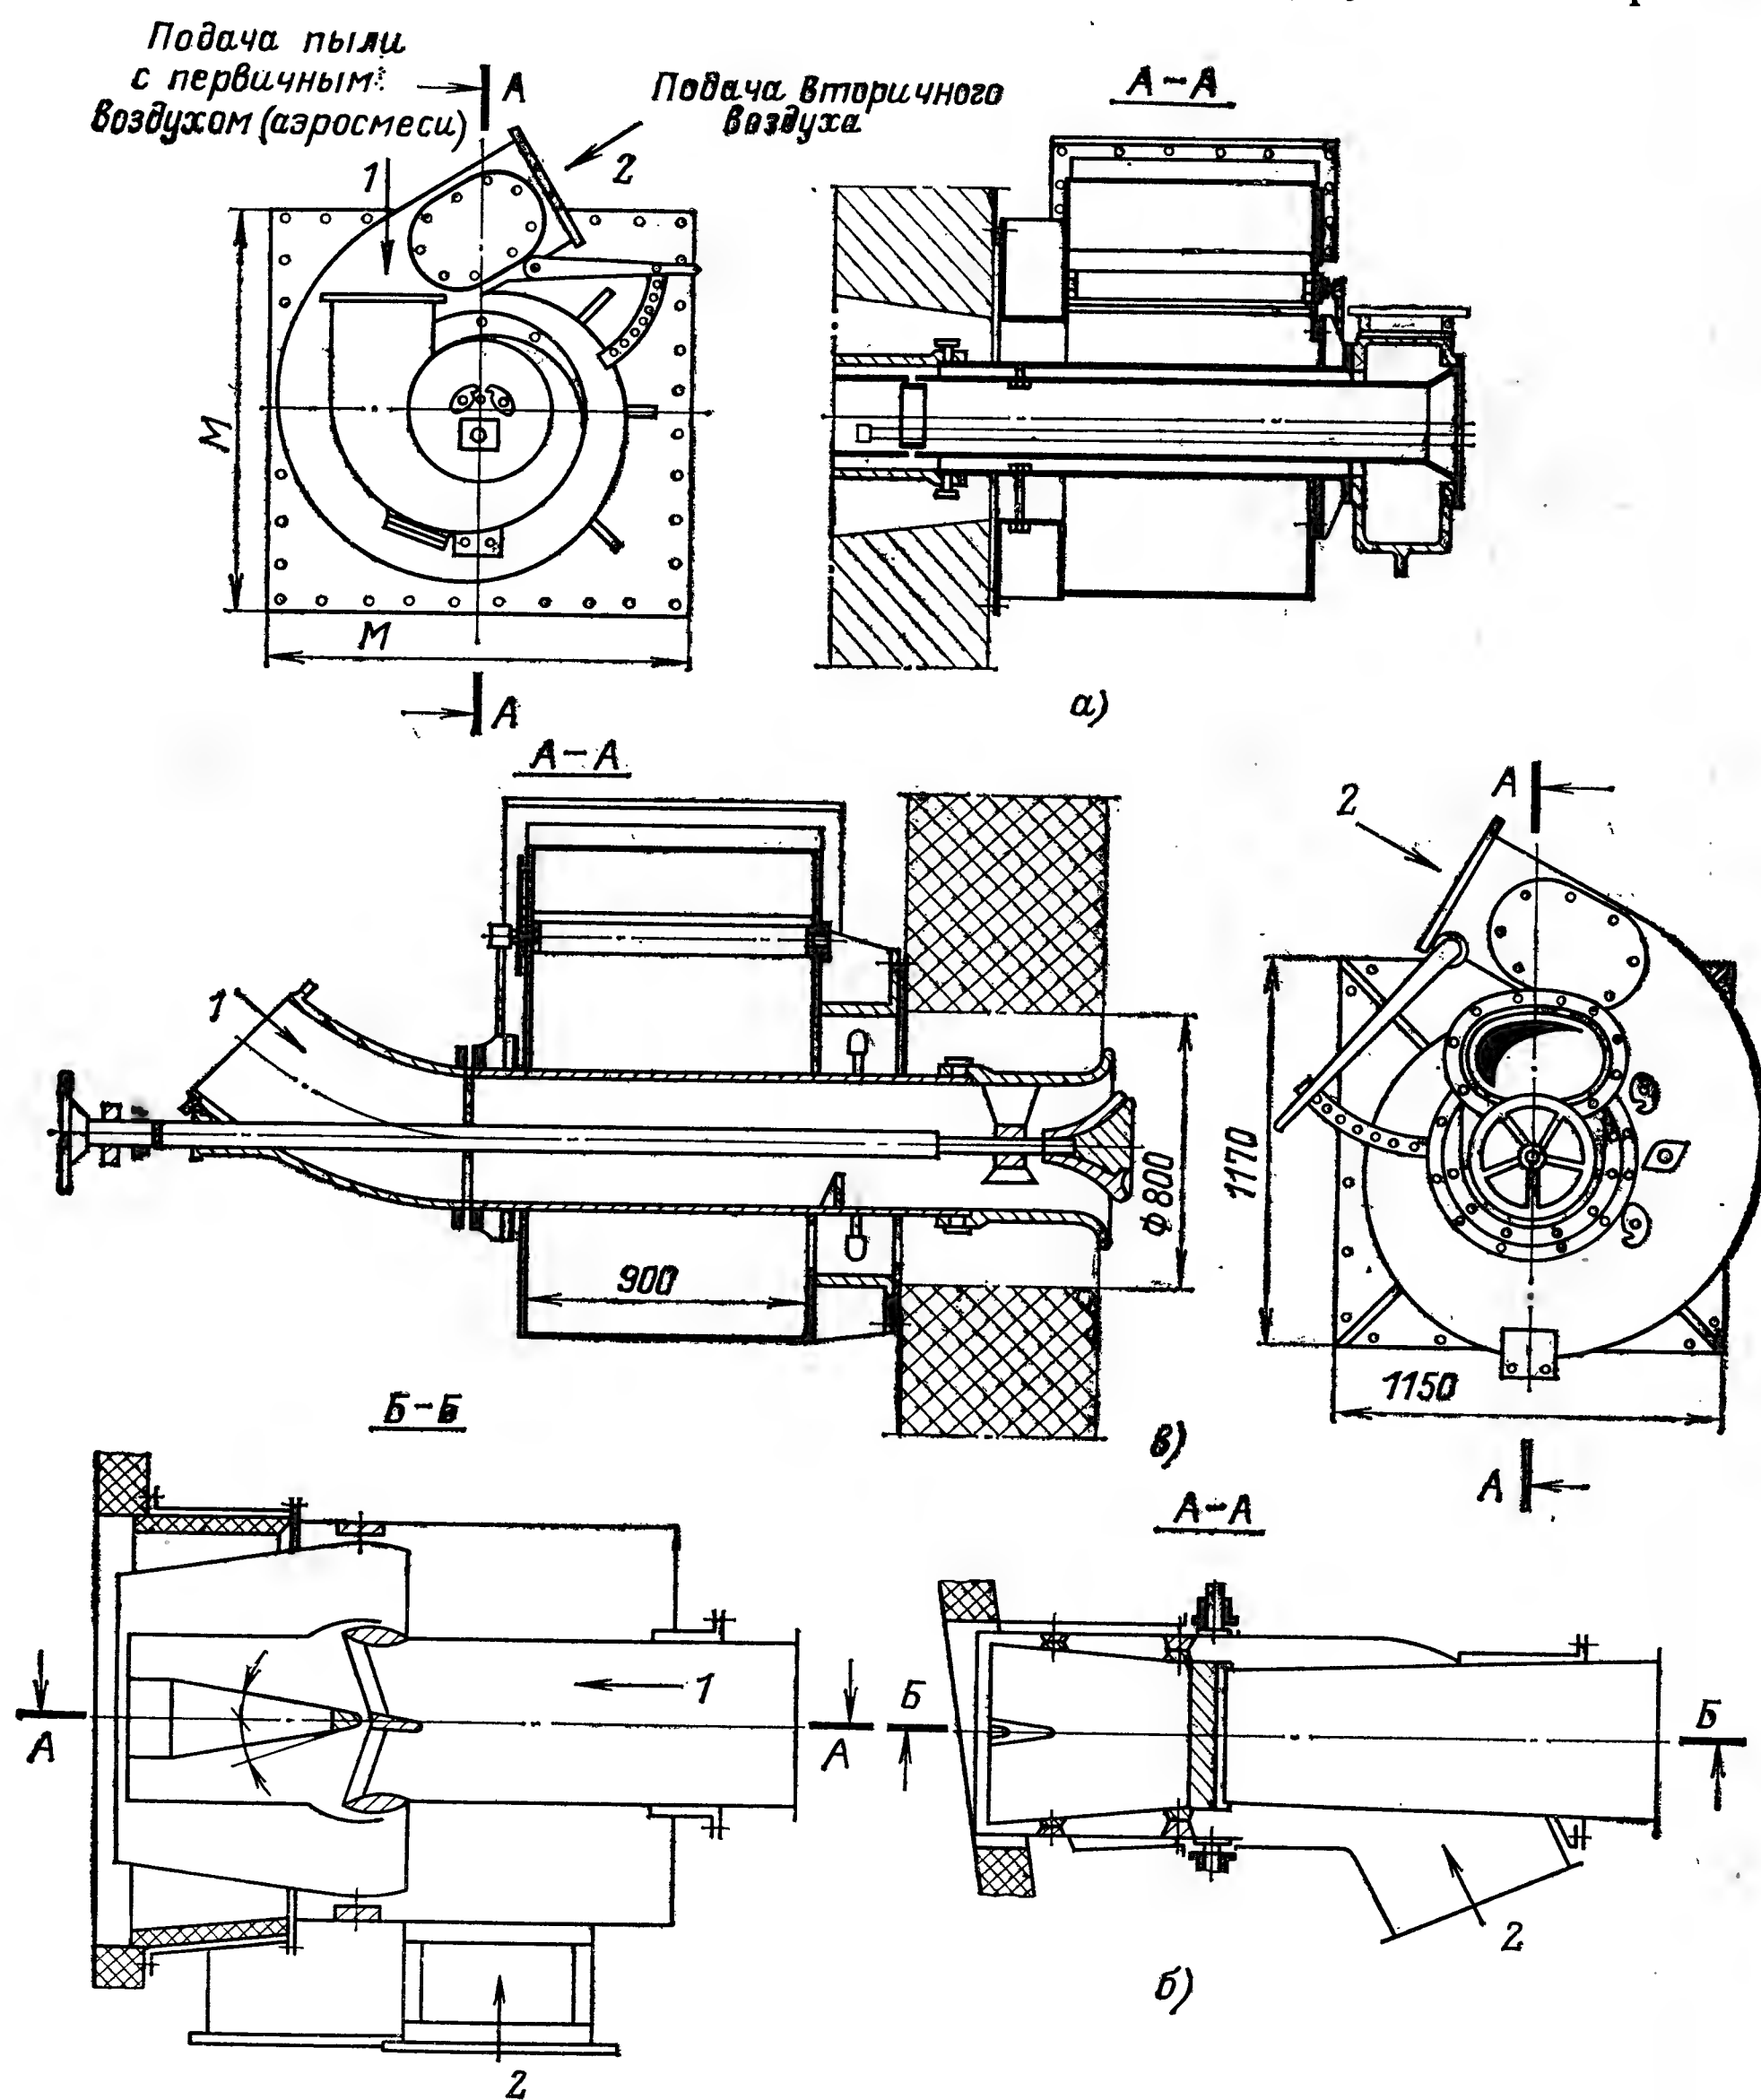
Основные типы горелок для пыли твердого топлива при сжигании его в камерной топке.
